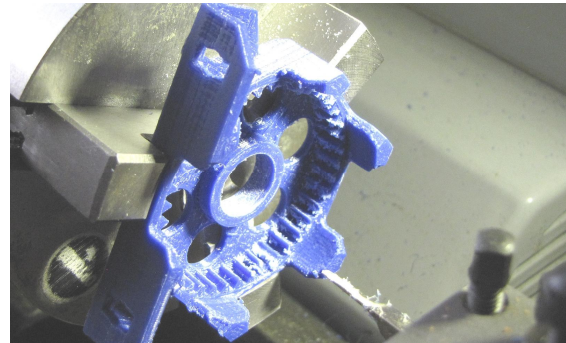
Das Sechseckige Gehäuse passt ins dreieckige Spannfutter
